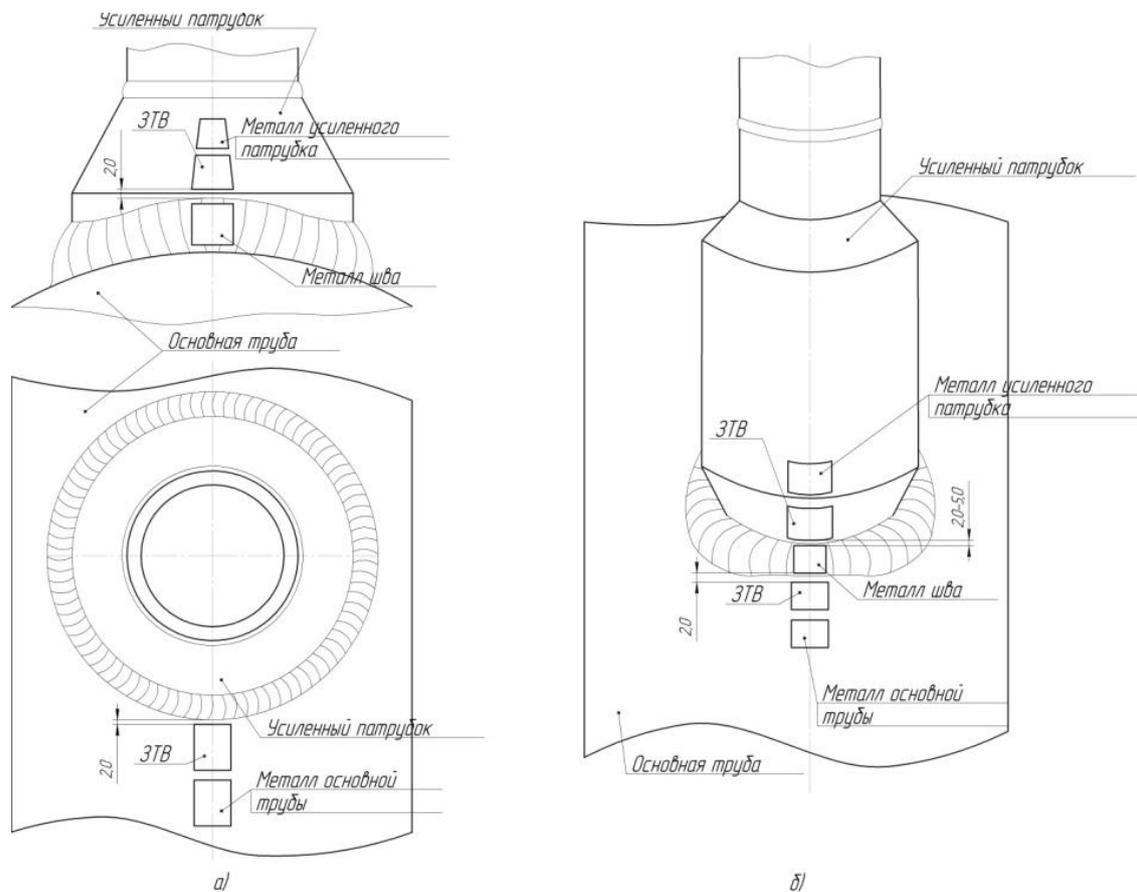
Схема расположения участков для замеров твердости в угловых сварных соединениях «труба - усиленный патрубок»
